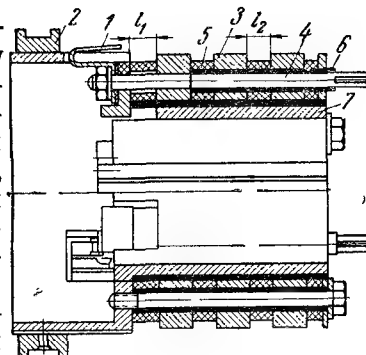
Контактные кольца с пружинными контактами, собранные на общей втулке. 1 — пружинный контакт; 2 — короткозамыкающее кольцо; 3 — контактное кольцо; 4 — контактный болт; 5 — изоляционная шайба; 6 — изоляционная втулка болта; 7 — втулка.
